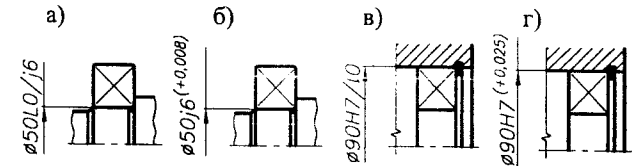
Обозначение посадок подшипников на сборочных чертежах: а), б) - на валу; в), г) - в корпусе
